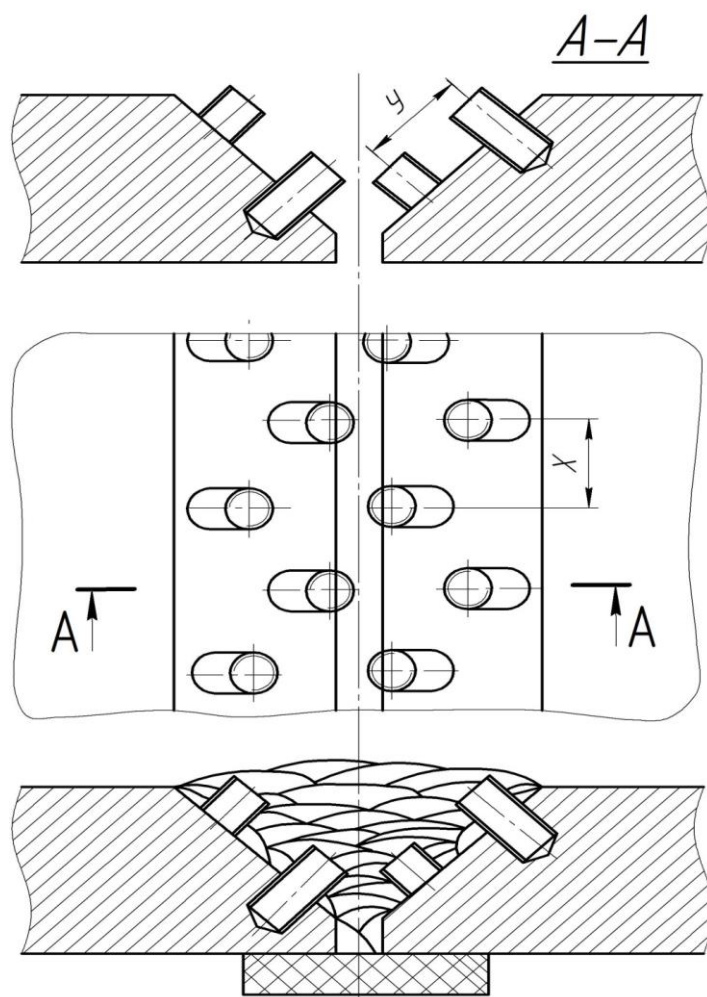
Схема розташування шпильок і зварювання розробки;
